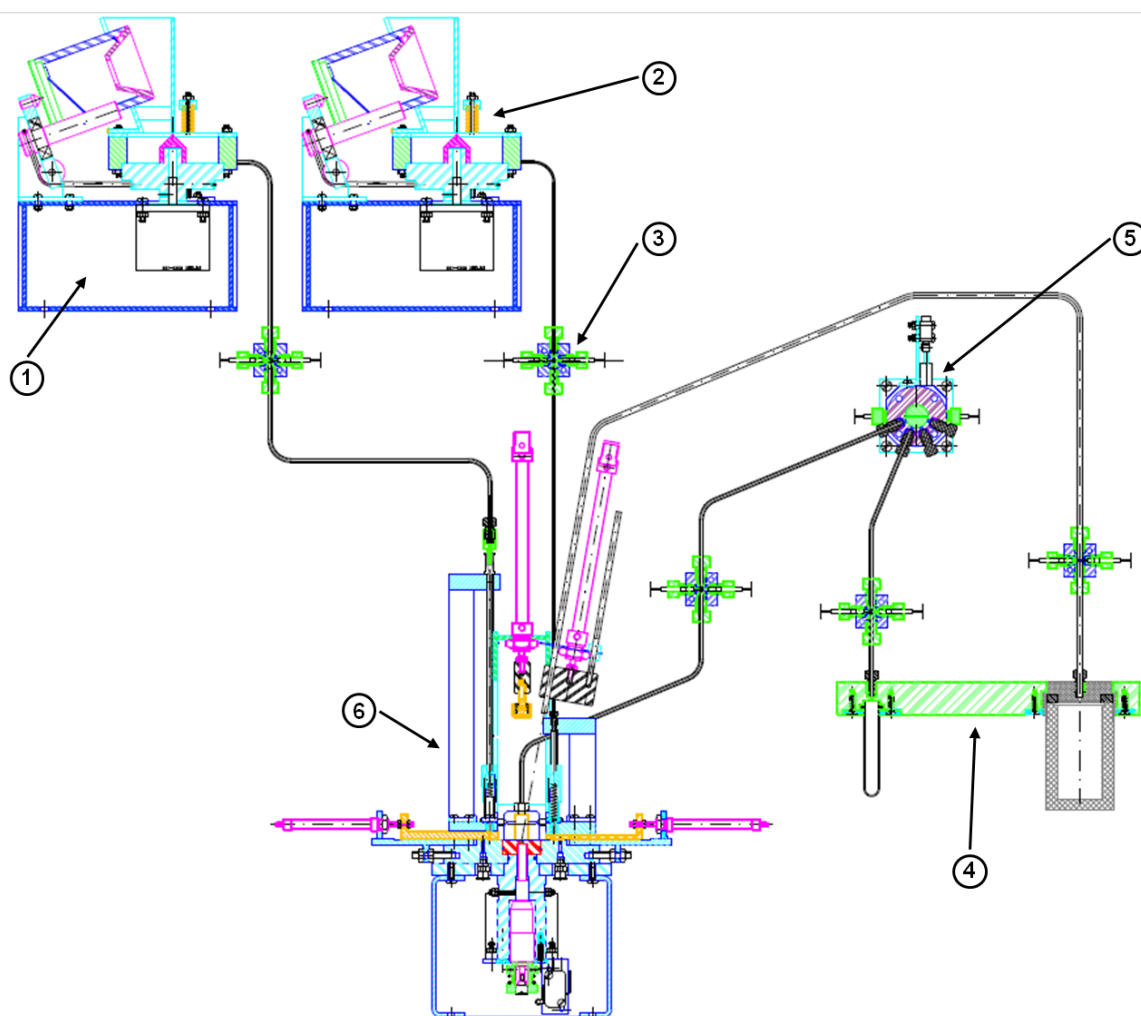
Sistema de soldagem a laser modificado constituído por: seletor e alimentador de cânulas (1), seletor e alimentador de fontes (2), suporte para sensor em fibra óptica (3), receptor de fontes seladas (4), distribuidor inversor (5) e dispositivo de soldagem (6)
